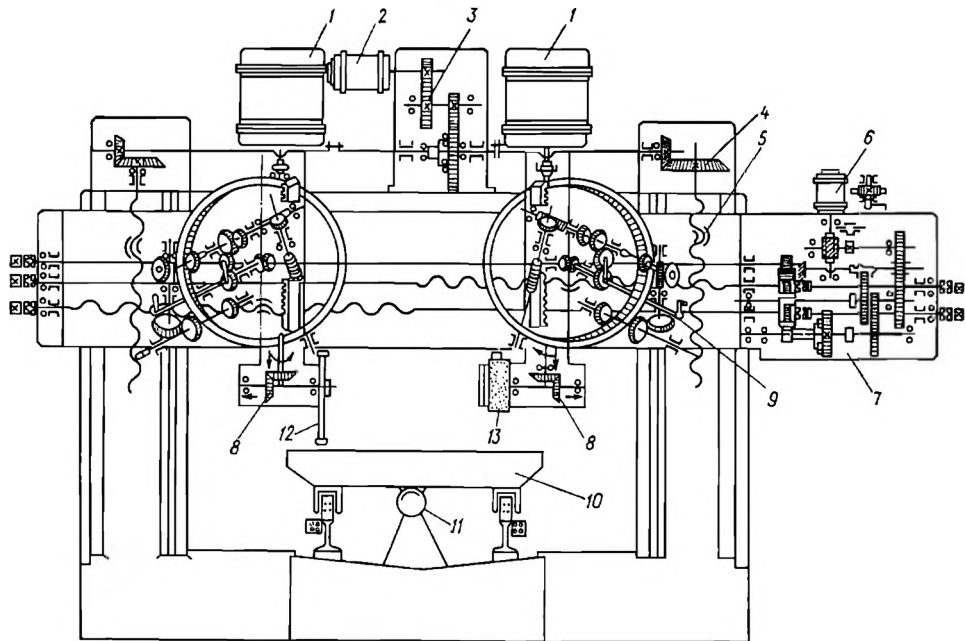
Кинематическая схема фрезерно-окантовочного портального станка модели ГФ-50
